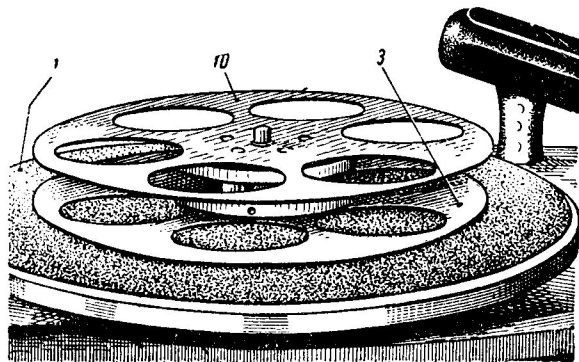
Общий вид приставки: 1 — диск проигрывателя; 3 — ведущий диск; 10 — ведомый диск
